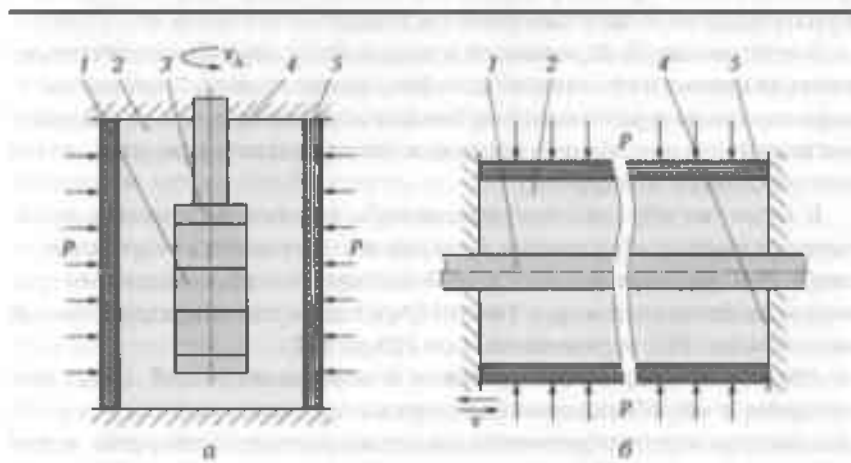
Основные схемы обработки деталей камерным способом:
